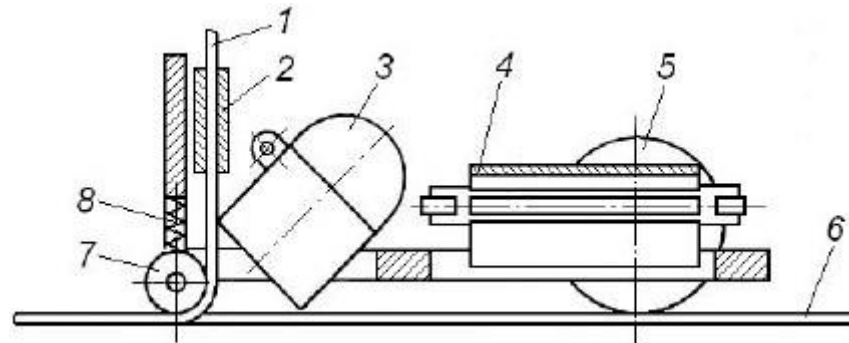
Схема сварки листового термопласта световым излучением с применением присадочного материала: 1– присадочный пруток; 2– подогреватель; 3– точечный излучатель; 4– стержневой излучатель; 5,7– ролики; 6– листовой термопласт; 8 –пружина
